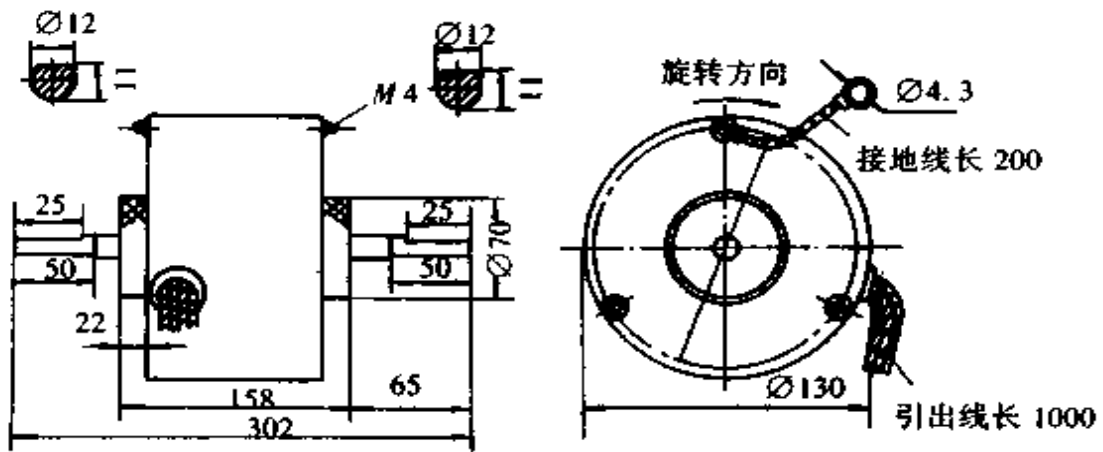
YK-100-6D 型电动机外形和安装尺寸
